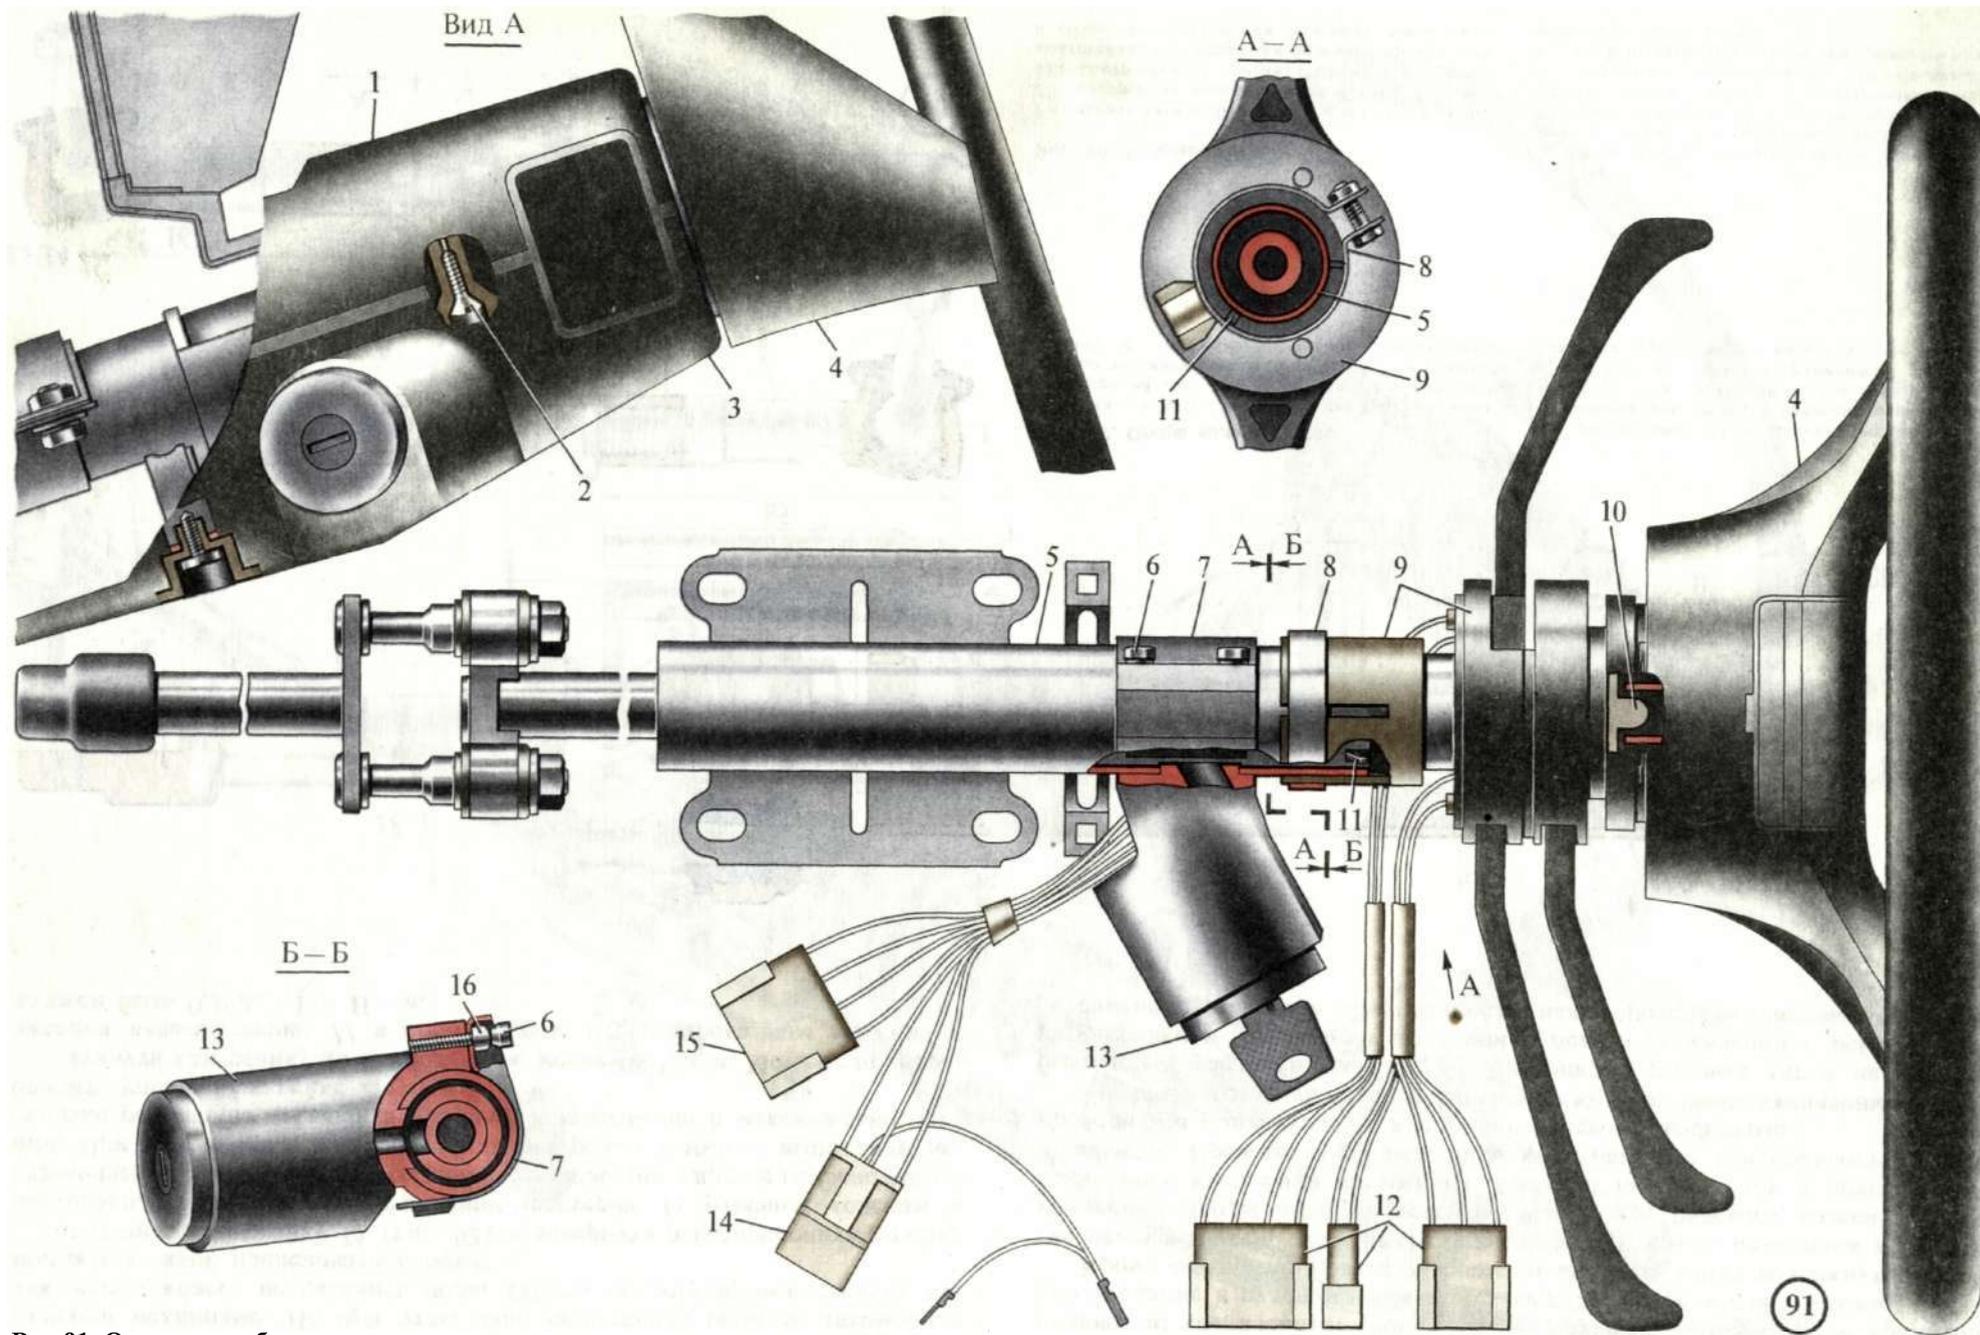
Опора вала в сборе с выключателем зажигания, рулевым колесом и переключателем:
